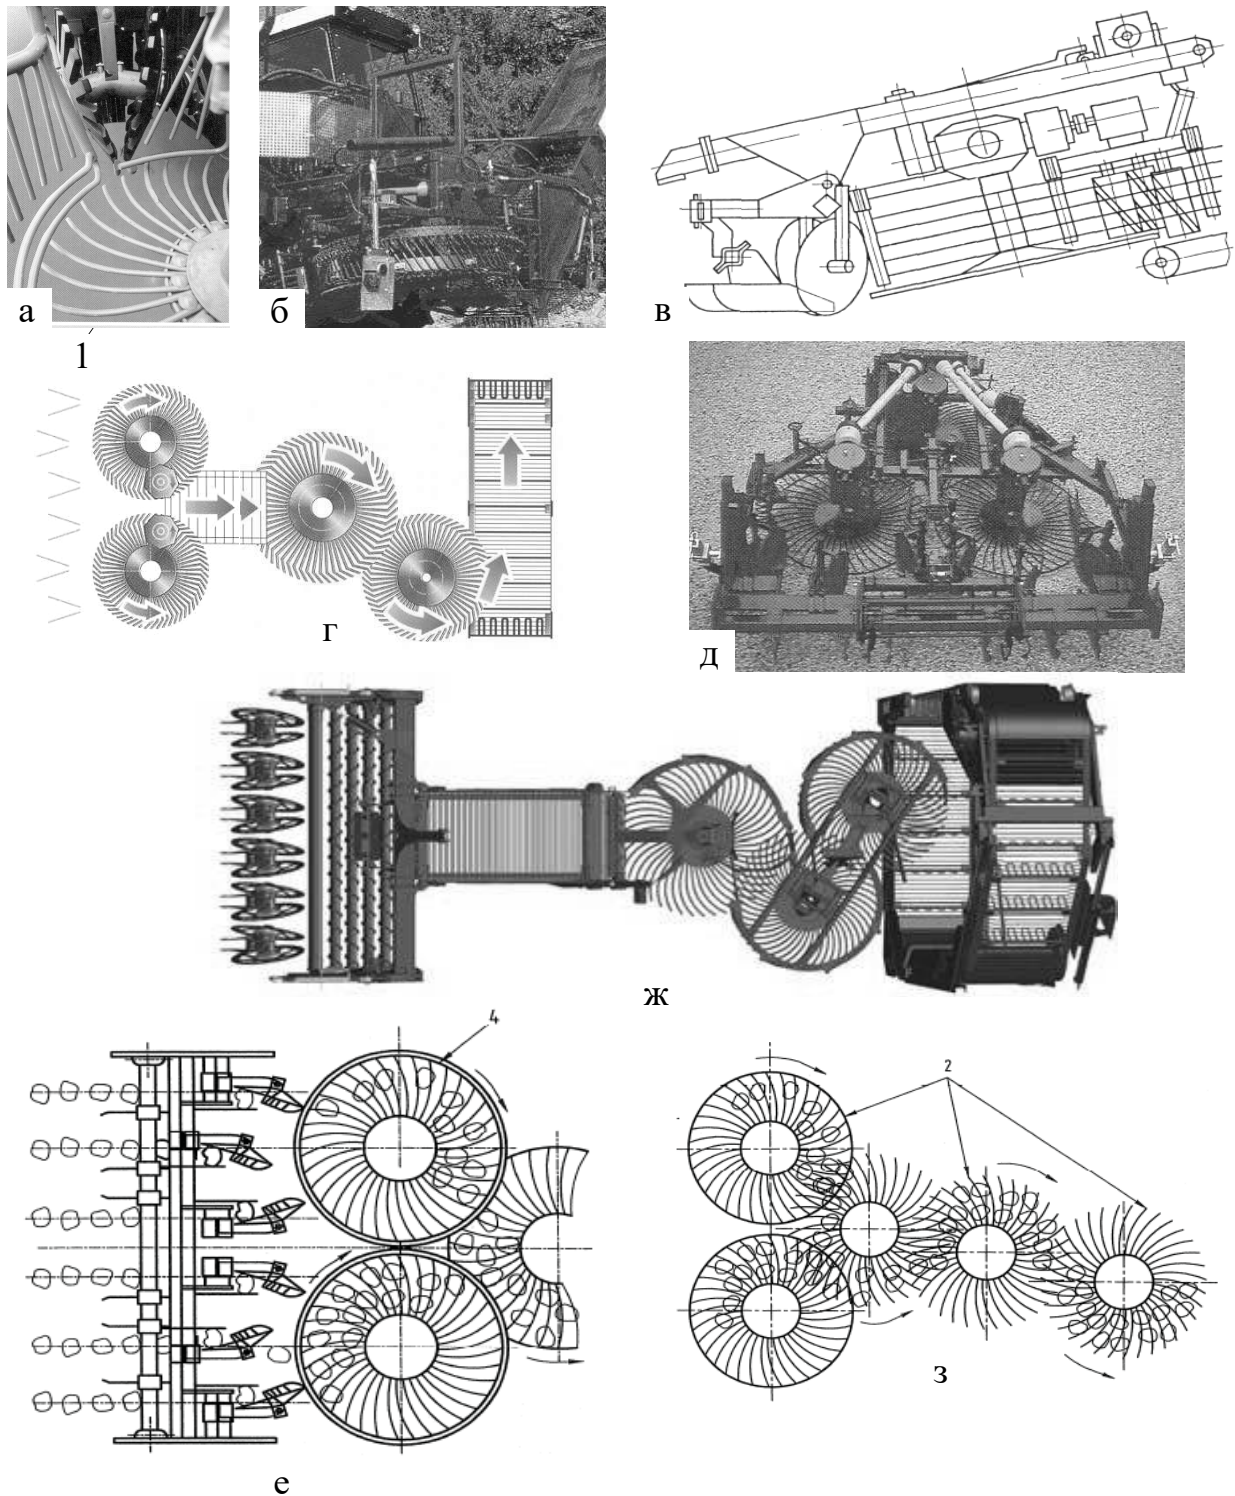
Загальний вигляд і конструктивні схеми роторних очисників
